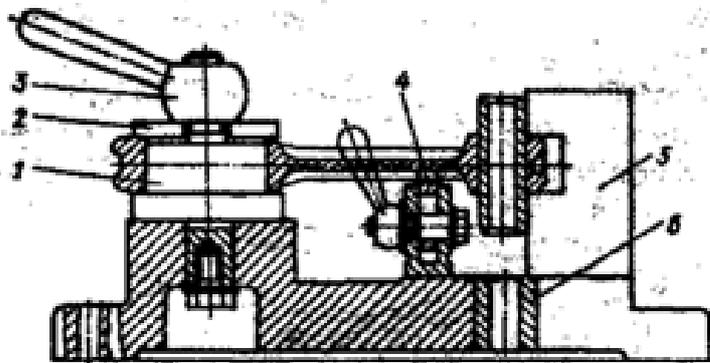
Приспособление для контроля и рихтовки шатунов: 1 - оправка; 2 - шайба; 3 - зажимная рукоятка; 4 - опора; 5 - шаблон; 6 - направляющая втулка
